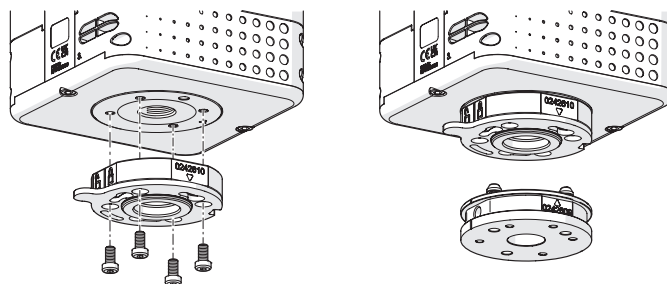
Der Werkzeugwechsler ist am piCOBOT® L befestigt.
